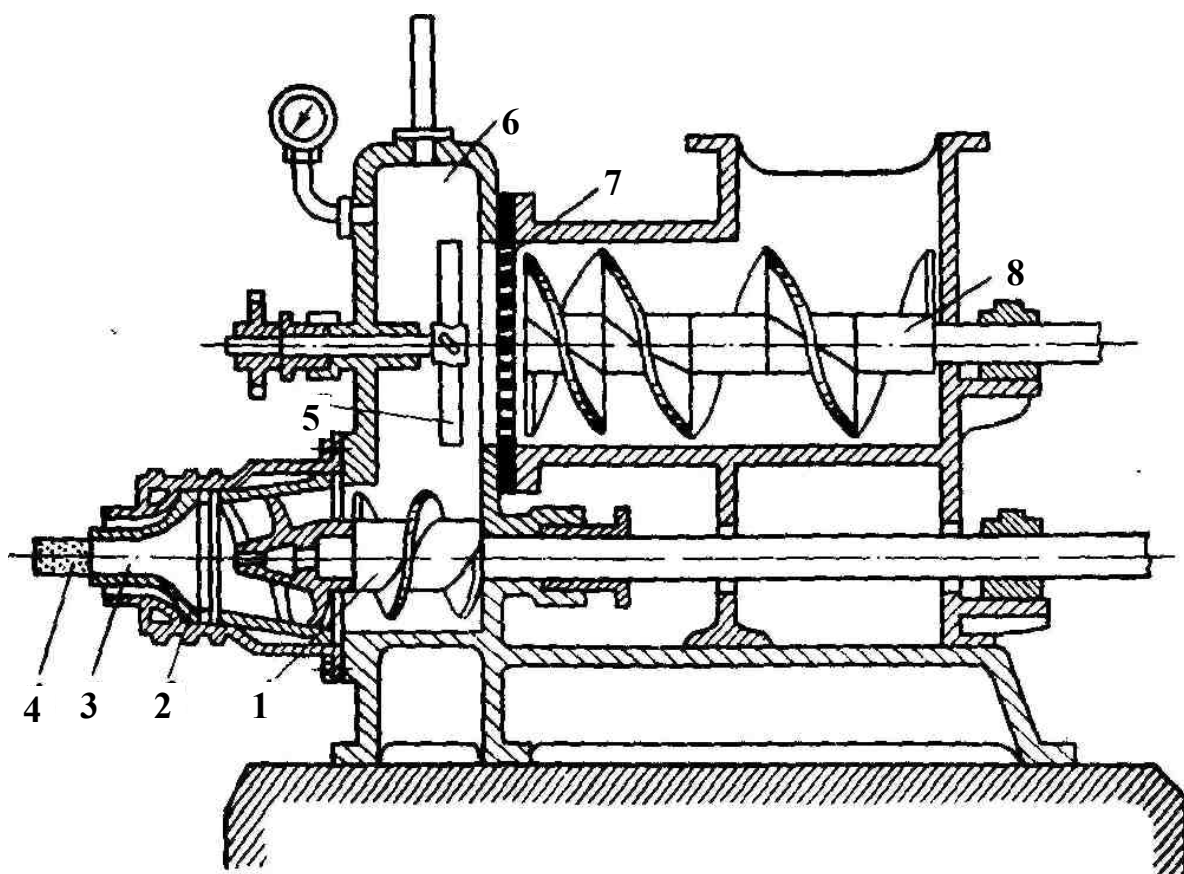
Стрічковий вакуумний прес: 1 – гвинтовий вал; 2 – конусна головка; 3 – мундштук; 4 – глиняний брус; 5 – ніж; 6 – вакуумна камера; 7 – решітка; 8 – гвинтовий конвеєр
